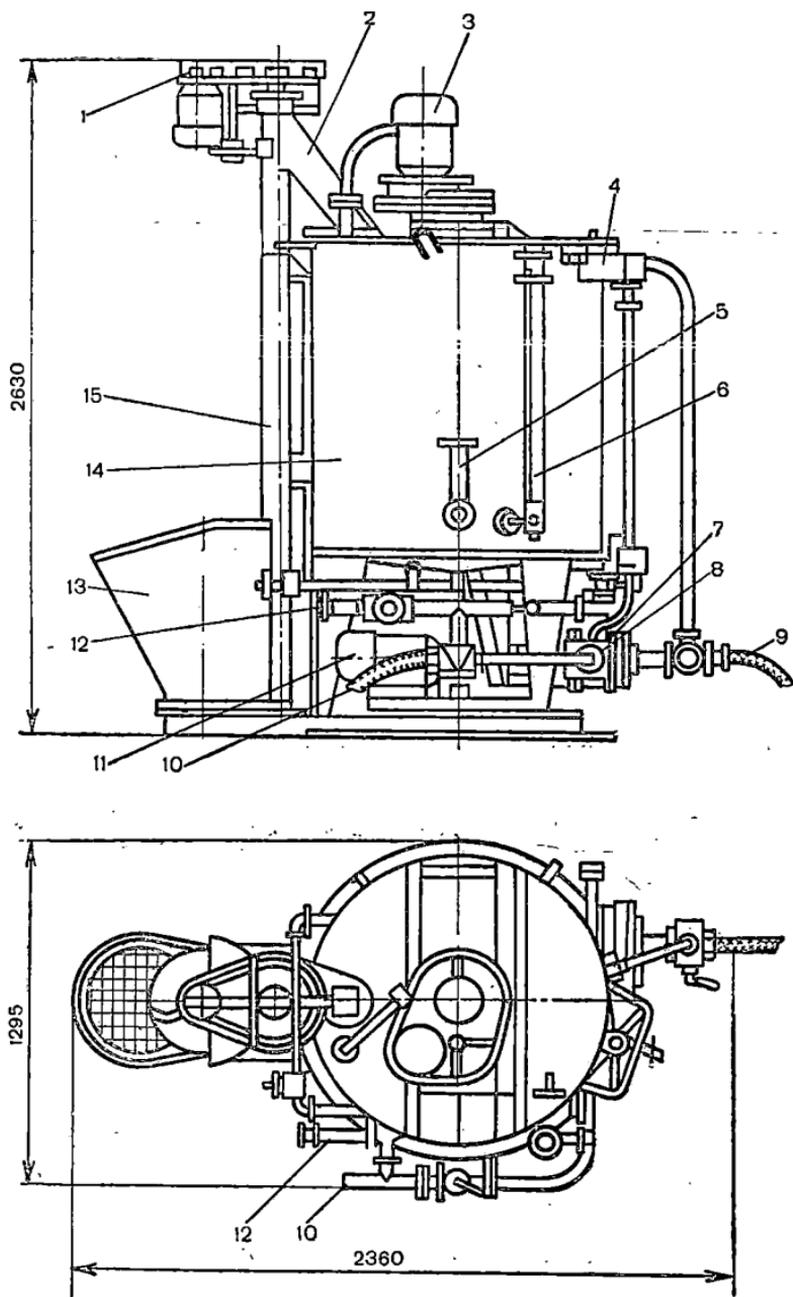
Агрегат АЗМ-0,8 для приготовления заменителя молока: 1 — привод шнека; 2 — течка; 3 — двигатель с редуктором; 4 — бачок для жиров; 5 — термометр; 6 — указатель уровня готового продукта; 7 — насос-эмульгатор; 8 — фильтр; 9 — рукав выдачи готового продукта; 10 — рукав для обраты; 11 — электродвигатель насоса-эмульгатора; 12 — паропроводящий патрубок; 13 — приемный бункер; 14 — наружный корпус; 15 — загрузочный шнек
